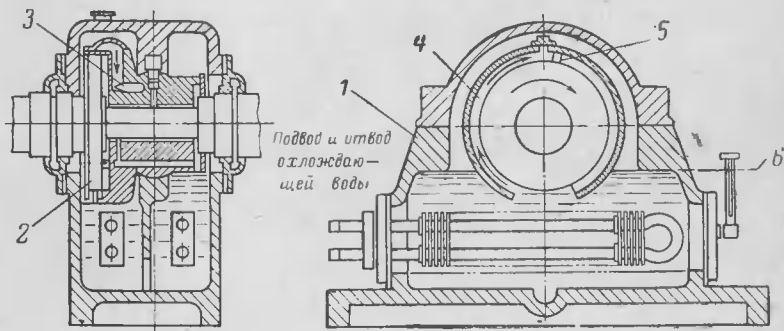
Подшипник двигателя типа АТМ с дисковой смазкой.
